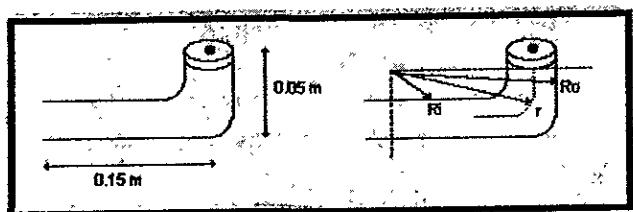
DIMENSIONES DEL CODO DE TUBO
